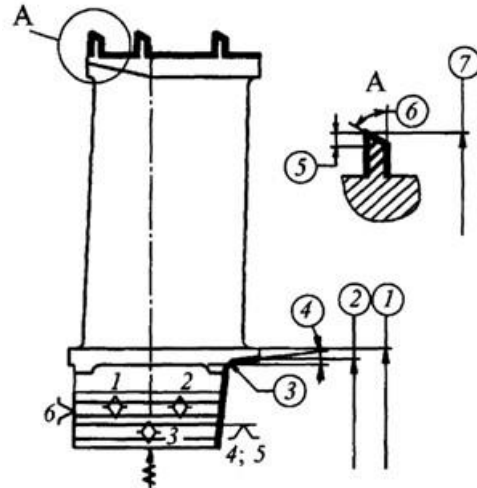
схема обробки циліндричних поверхонь лопатки.
